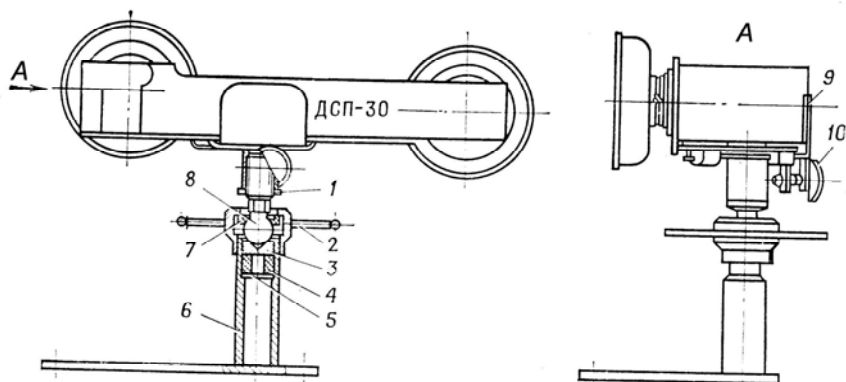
Приспособление для крепления дальномера ДСП-30:
